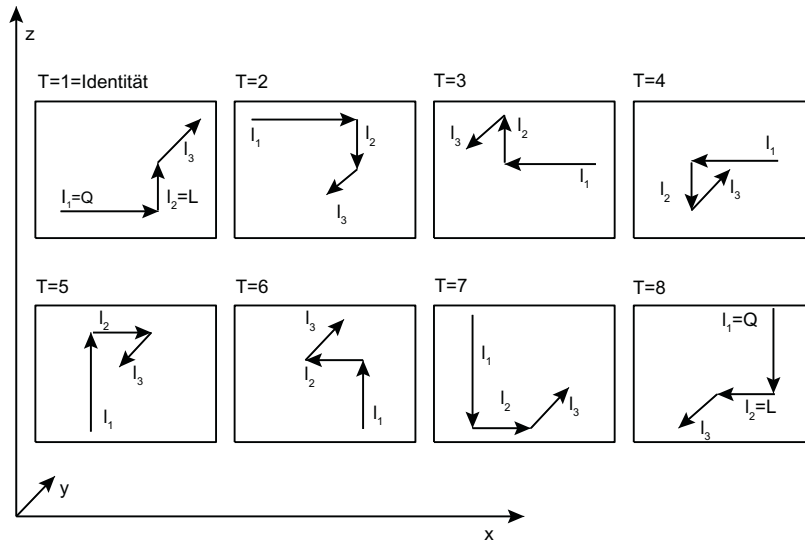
Die 8 definierten Transformationen (T = 1...8) für den Adapter mit G 18 und für ein Drehwerkzeug. Es werden die Zuordnungen der Werkzeuglängen I1, I2, I3 auf die Geometrieachsen x, y, z gezeigt.
